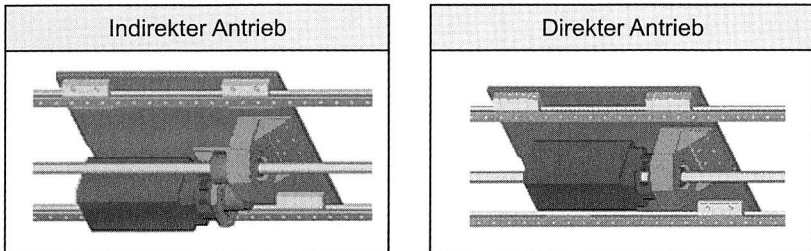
Systemlösungen mit angetriebener Spindelmutter (links: Servomotor; rechts: Hohlwellenmotor) [38], [39]
